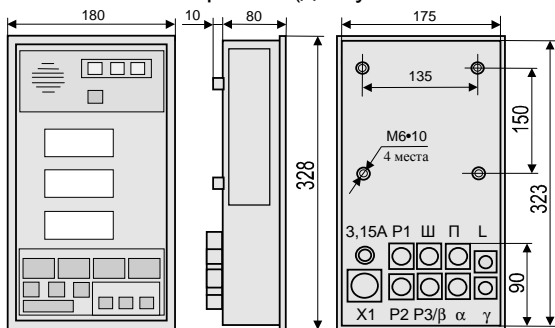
Габаритные и присоединительные размеры БОДа
